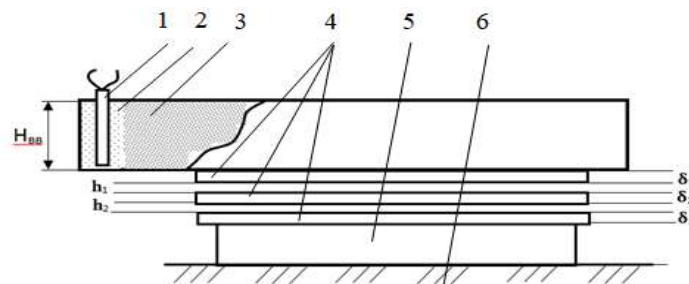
Схема сварки взрывом 3-слойного СММ с ВП:
